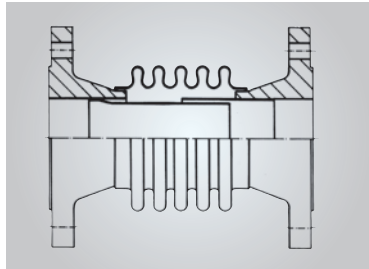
Axial-Kompensator mit Vorschweißflanschen
